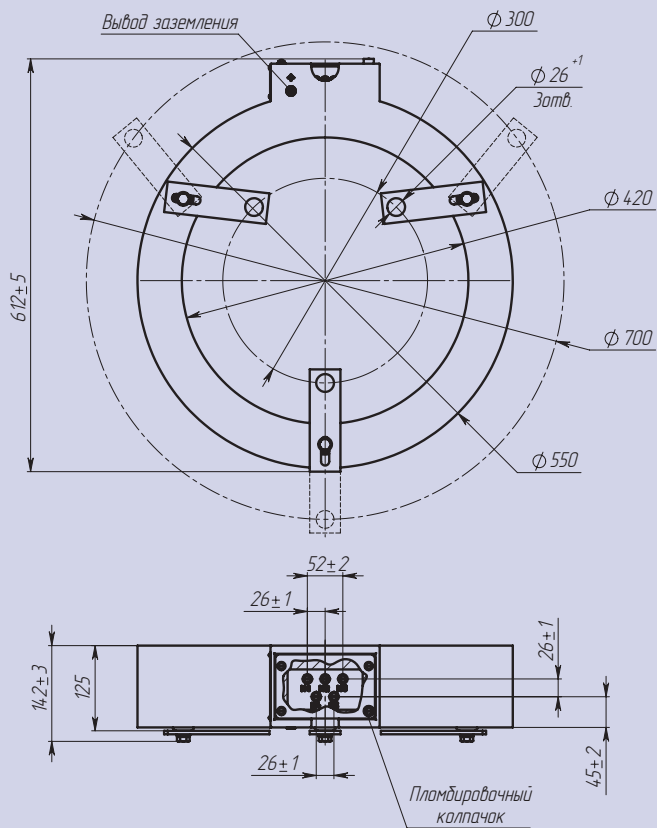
Габаритные, установочные и присоединительные размеры трансформатора ТВ-110-IX-3.2-1
